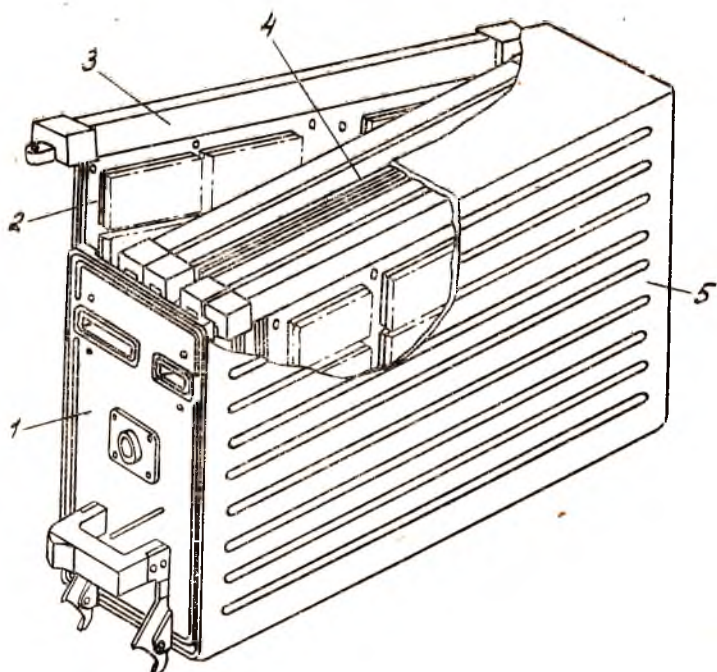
Герметичный блок книжной конструкции самолетной МЭА: 1 — передняя панель; 2 — печатная плата с микросхемами; 3 — воздуховод; 4 — соединительная печатная плата с гибким печатным кабелем; 5 — кожух
